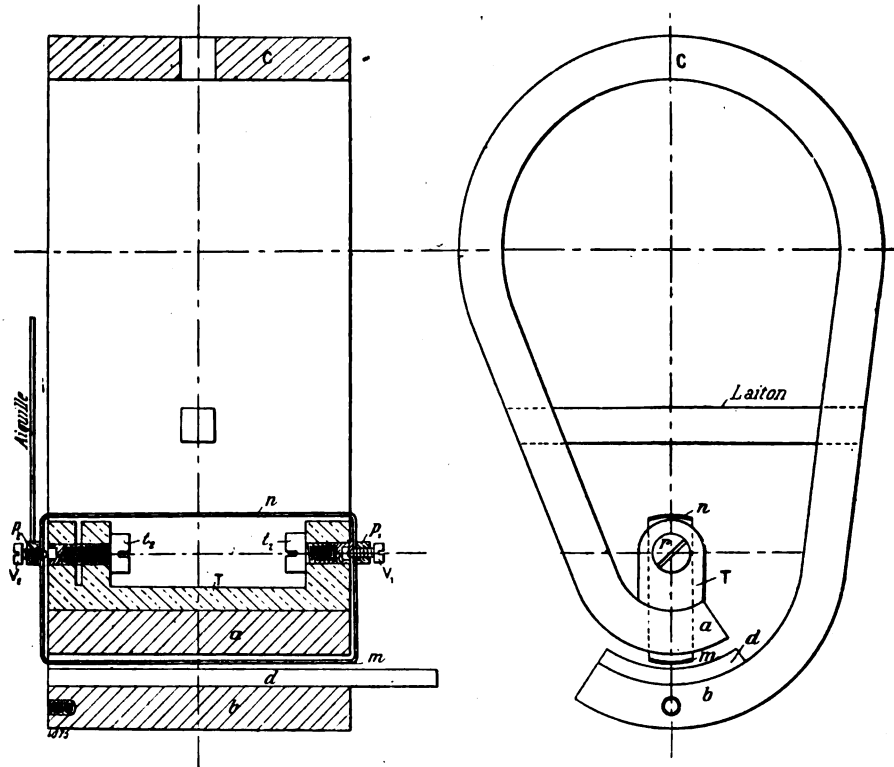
et 9. — Coupe et vue de face d'un galvanomètre Meylan.
